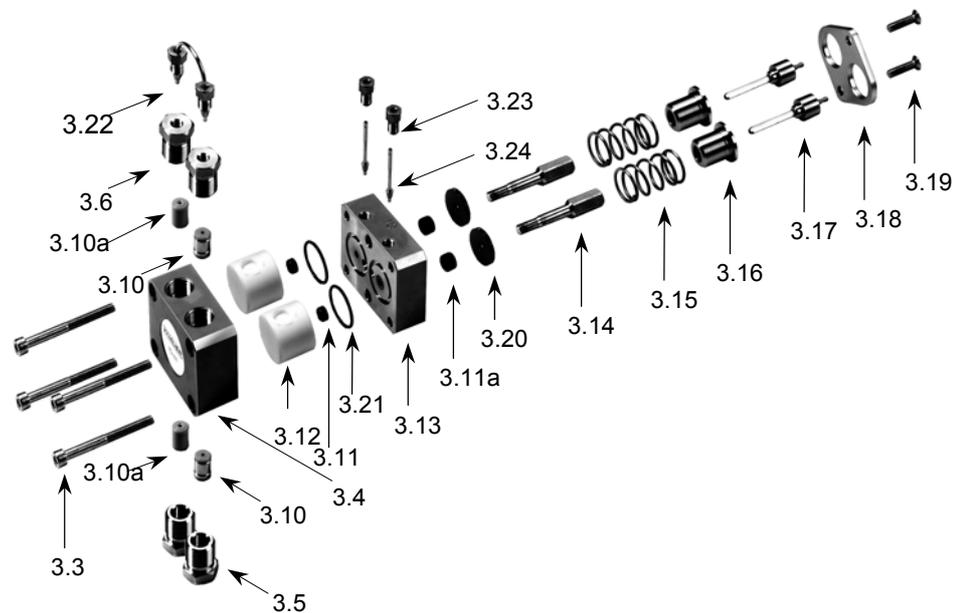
Explosionsdarstellung eines Pumpenkopfes
